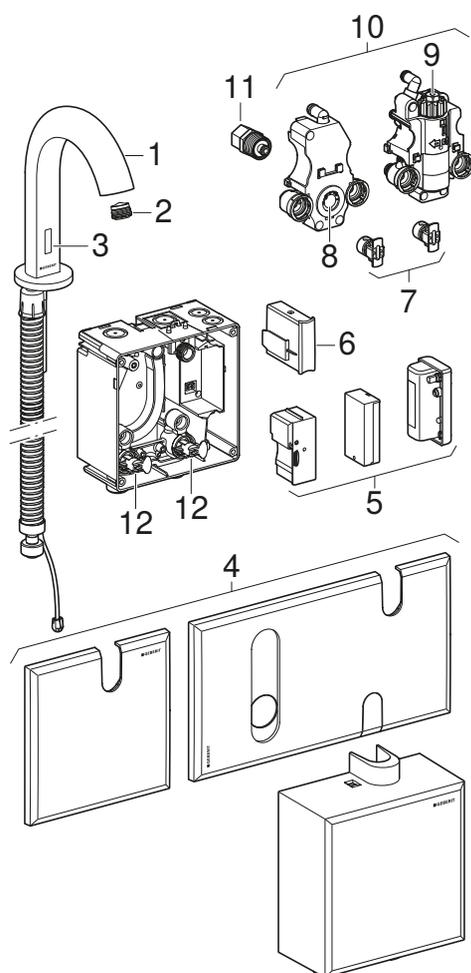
Rubinetterie per lavabo Geberit Piave e Brenta, montaggio a pianale
